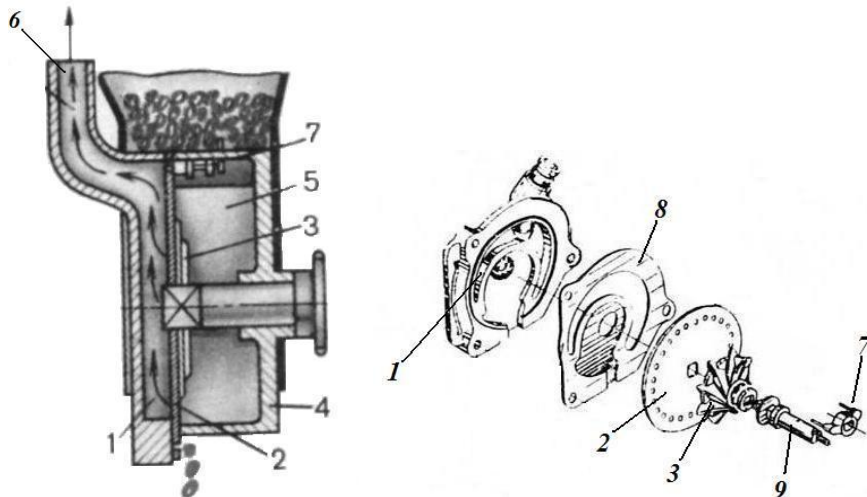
Общий вид высевающего аппарата сеялки СУПН-8 и схема его рабочего процесса: 1 – вакуумная камера; 2 – диск; 3 – ворошитель; 4 – корпус; 5 – заборная камера; 6 – патрубок; 7 – вилка отражательная; 8 – уплотнитель; 9 – вал привода
